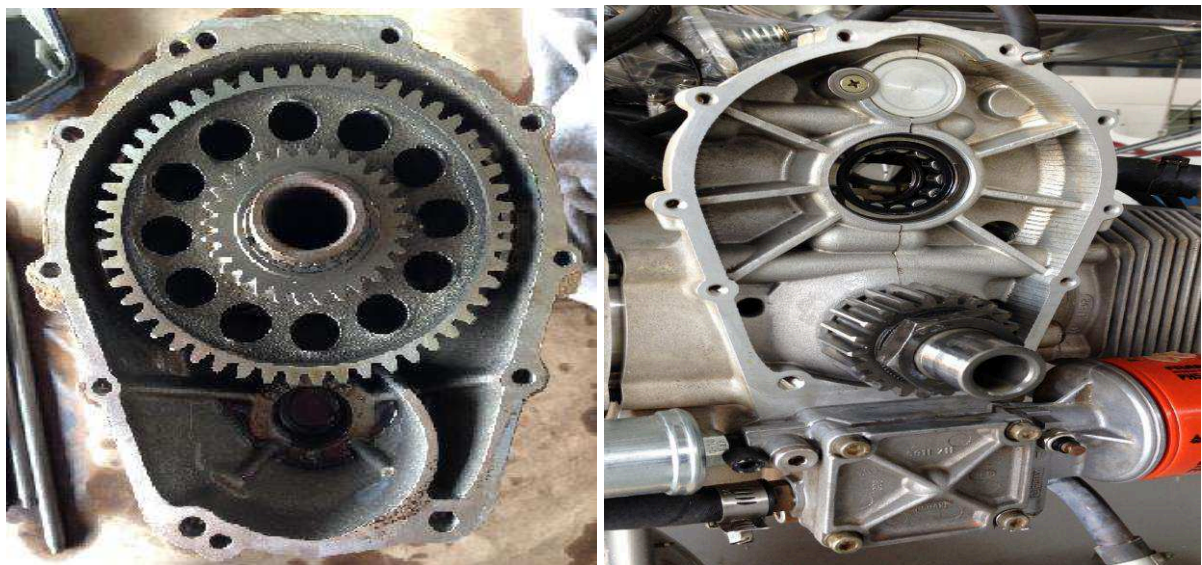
Caixa de redução com componentes (esquerda) e motor com componentes (direita)
